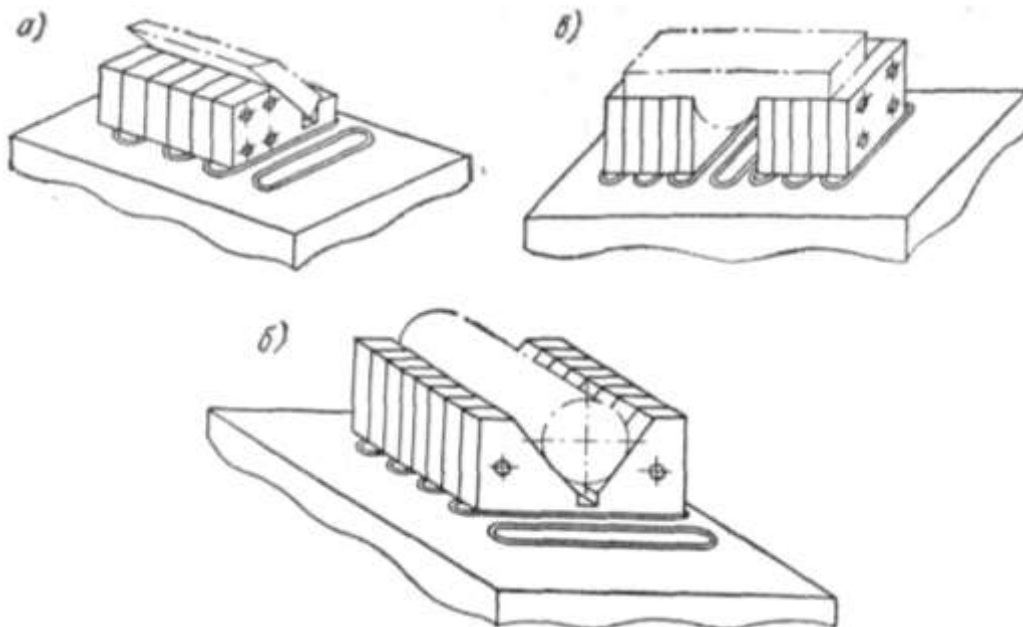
Наладки к магнитным плитам, изменяющие их базовую поверхность: *а* — односторонняя призма для плоских деталей; *б* — призма для деталей типа валов и втулок; *в* — кубики для деталей с выступами
